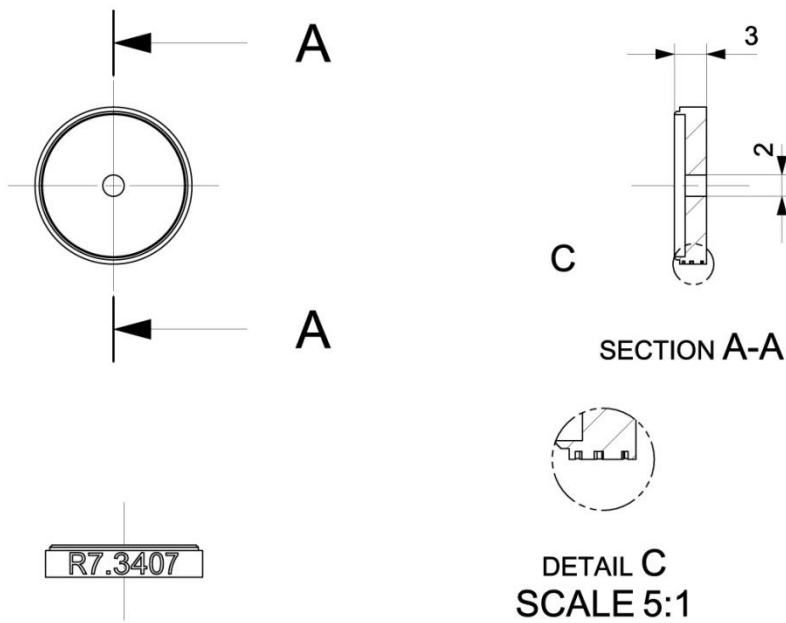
Technische Zeichnung Kappchen für Aktormodulgehäuse V02T05
